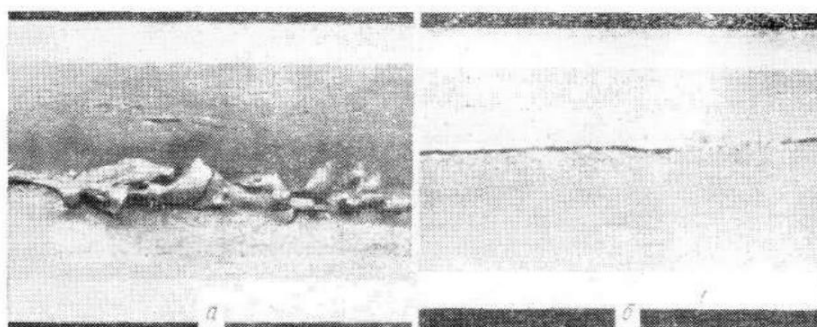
Расслоение металла у внутренней поверхности гильз из стали марки ШХ15 по ГОСТ 4727–83 [39] [36]
